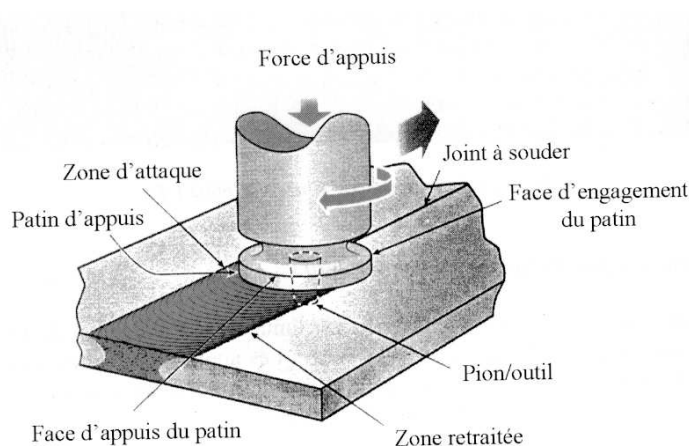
Le soudage par friction et malaxage [Blondeau, 2001b].
